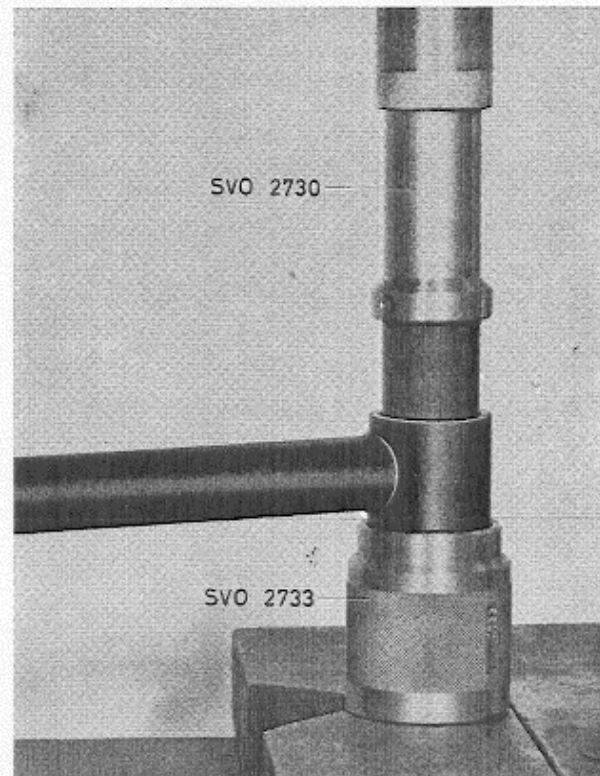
Einpressen der kleineren Lagerbuchse für die Panhardstange
